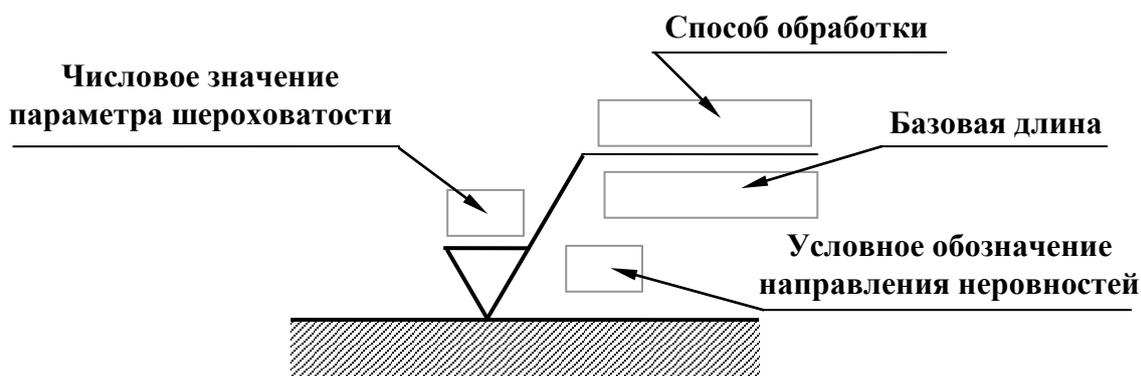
Общий вид структуры обозначения шероховатости поверхностей
